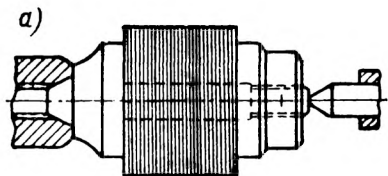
Оправки для обработки по наружному диаметру заготовок зубчатых колес.
